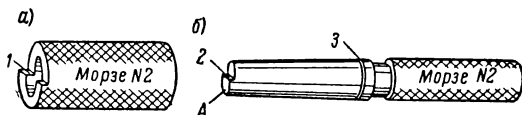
Конические калибры для проверки наружных и внутренних конических поверхностей.
